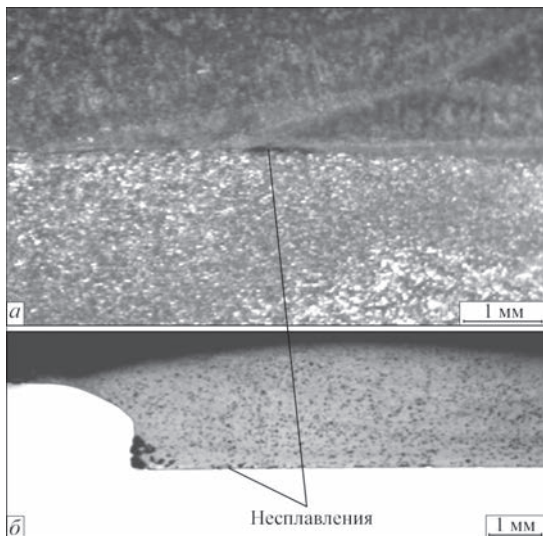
Несплавления на границе соединения основного и наплавленного металлов (4011) при плазменно-порошковой (а) и лазерно-порошковой наплавке (б) [4]
